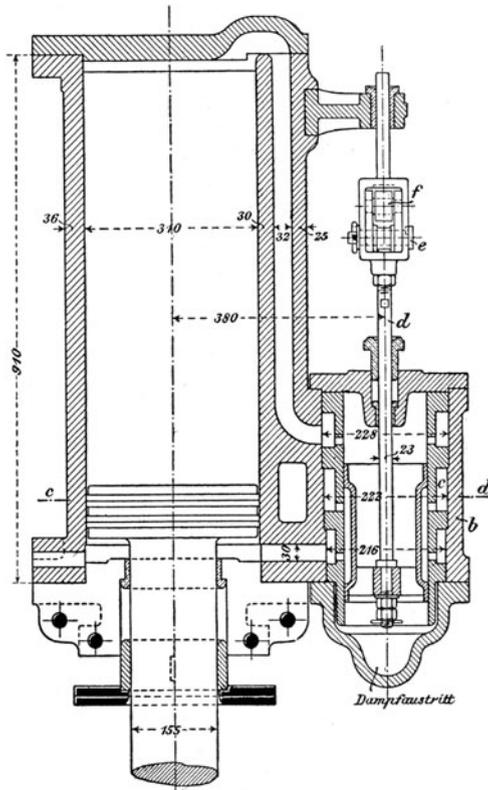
Dampfhammer mit Brinkmann-Steuerung.
